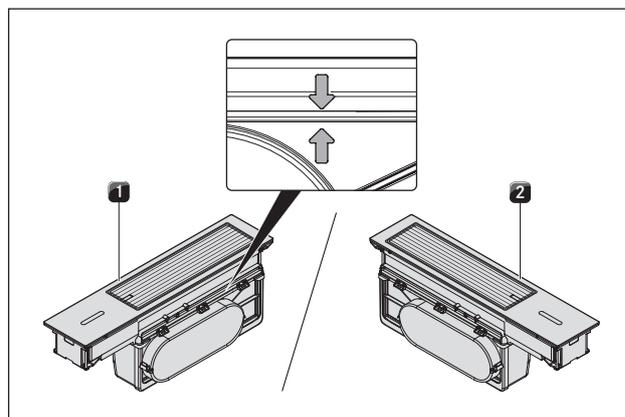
Extractor de superficie CKA2 ensamblado
